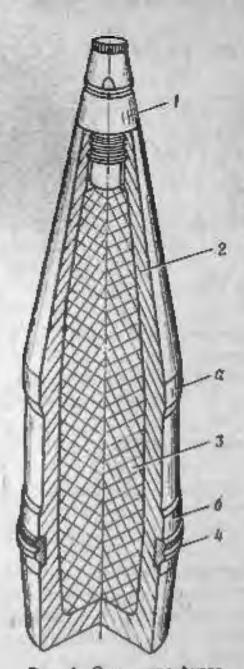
Осколочно-фугвсный снаряд ОФ-462: — варыватель: 2— корпус, 3— разрывной заряд; 4 ведущий поясок; а—верхнее центрующее утрящевие: 6— вижнее центрую-
